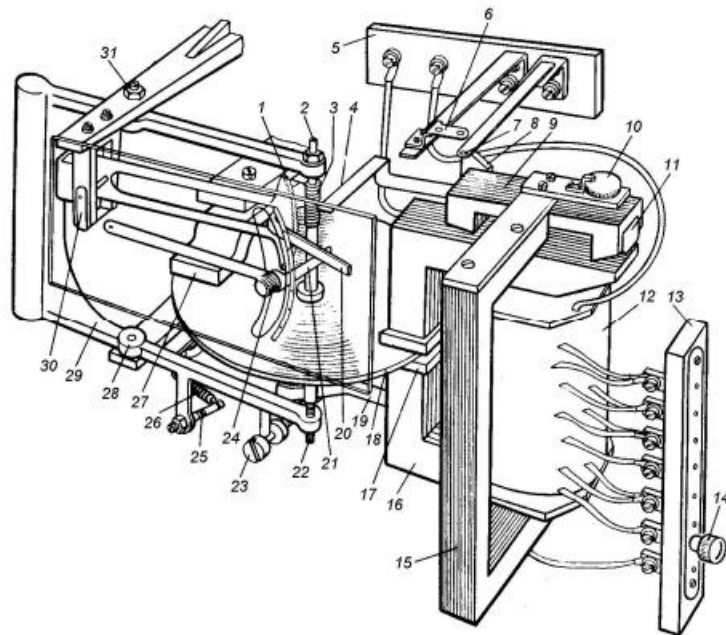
Конструкція реле РТ-80, де 1 - зубчастий сектор; 2 - верхня опора диску; 3 - черв'як; 4 - фігурний важіль; 5 - контактна колодка; 6 - нерухомий контакт; 7 - рухомий контакт; 8 - текстолітова пластина; 9 - якір відсічки; 10 - регулювальний гвинт відсічки; 11 - короткозамкнений виток якоря; 12 - котушка; 13 - штепсельний місток; 14 - штепсельний гвинт; 15 - шунт магнітопроводу; 16 - магнітопровід; 17 - екрани; 18 - диск; 19 - скоба; 20 - штовхач; 21 - опора; 22 - нижня опора диска; 23 - опорний гвинт; 24 - фасонний гвинт; 25 - регулювальний гвинт пружини; 26 - пружина; 27 - постійний магніт; 28 - нижня опора рамки; 29 - рамка; 30 - піввісь сектора; 31 - верхня опора рамки
